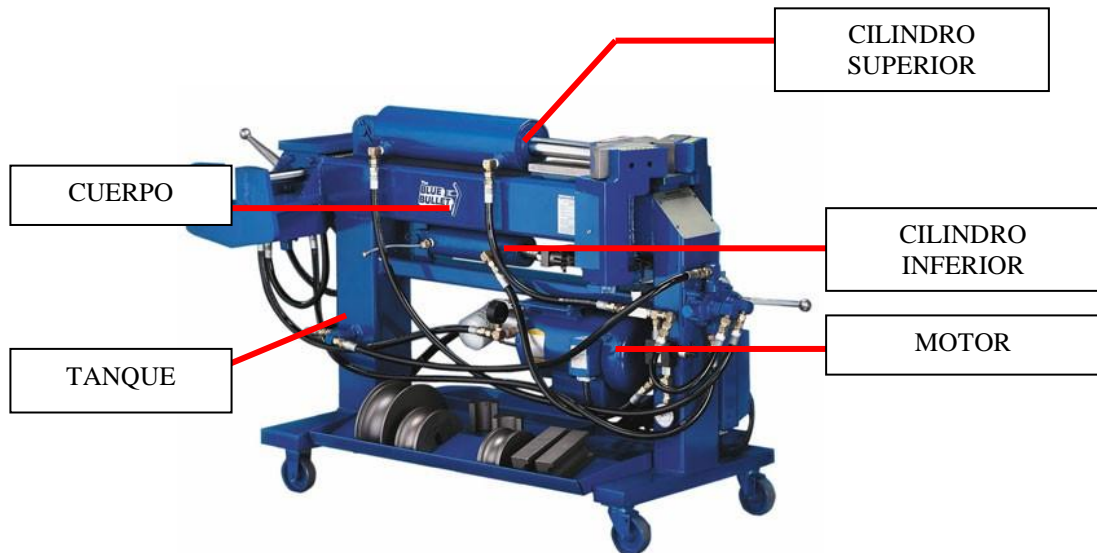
Partes constitutivas de la máquina BEND PAK modelo BB-2
